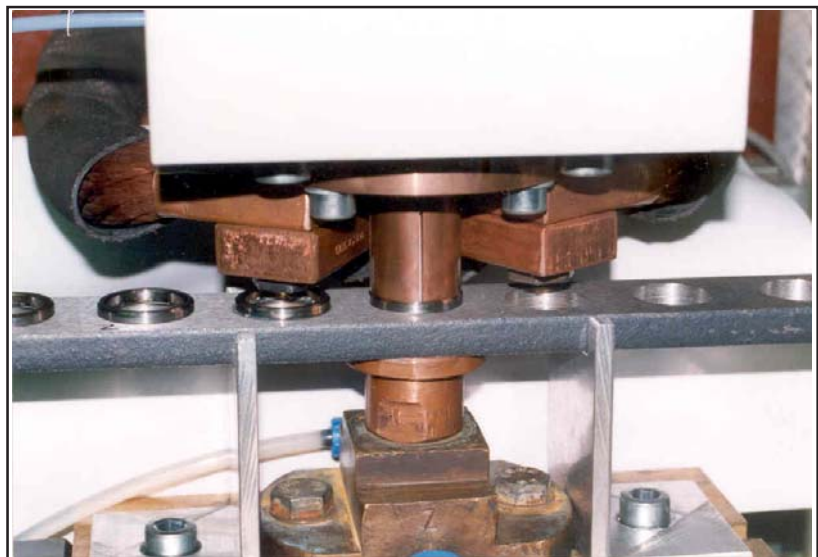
Spannvorrichtung zum Einschweißen von Sitzringen
